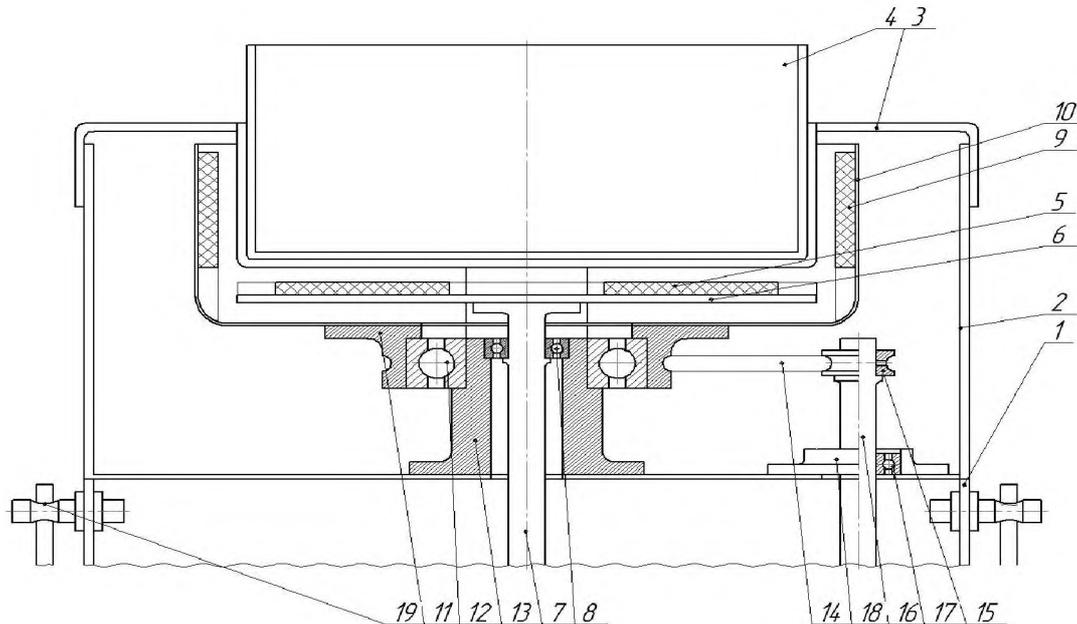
Установка для магнитной галтовки: 1 – основной корпус; 2 – верхняя часть корпуса; 3 – рабочий объем; 4 – рабочий контейнер; 5 – основная группа постоянных магнитов; 6 – подвижный диск; 7 – основной вал; 8 – подшипник; 9 – постоянные магниты; 10 – подвижный борт; 11 – втулка №1; 12 – основной подшипник; 13 – втулка №2; 14 – ремень; 15 – блок; 16 – вспомогательный вал; 17 – подшипник; 18 – втулка №3; 19 – поворотный механизм
